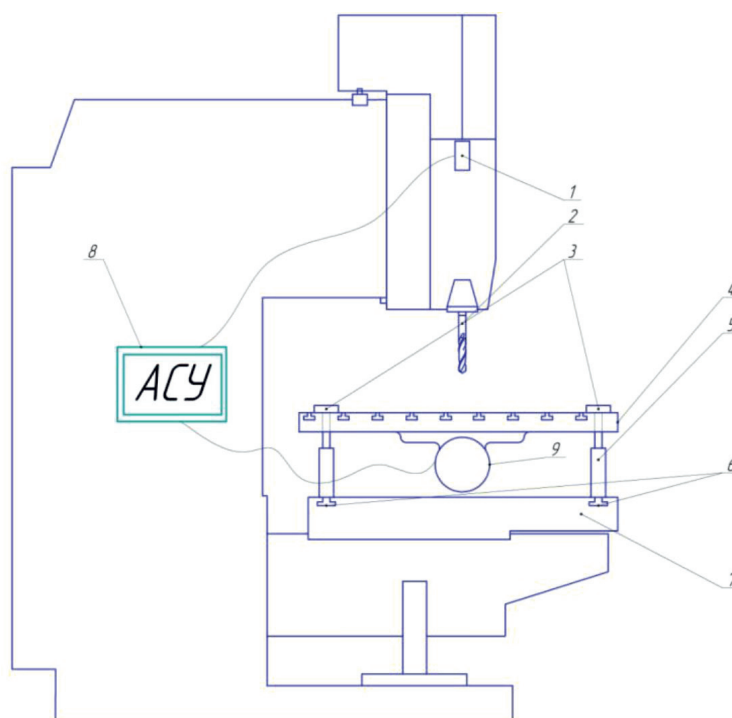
Схема вибропривода на фрезерном станке: 1 – датчик скорости шпинделя, 2 – инструмент, 3 – регулировочные болты, 4 – вибростол, 5 – втулки, 6 – крепежные болты, 7 – стол станка, 8 – автоматическая система управления, 9 – вибропривод
